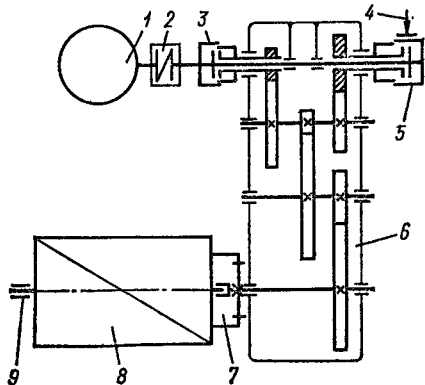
Схема двухскоростной лебедки с управляемыми муфтами 1 — двигатель; 2 — упругая муфта; 3, 5 — управляемые муфты; 4 — тормоз; 6 — редуктор; 7 — шарнирное соединение; 8 — барабан; 9 — подшипник барабана
